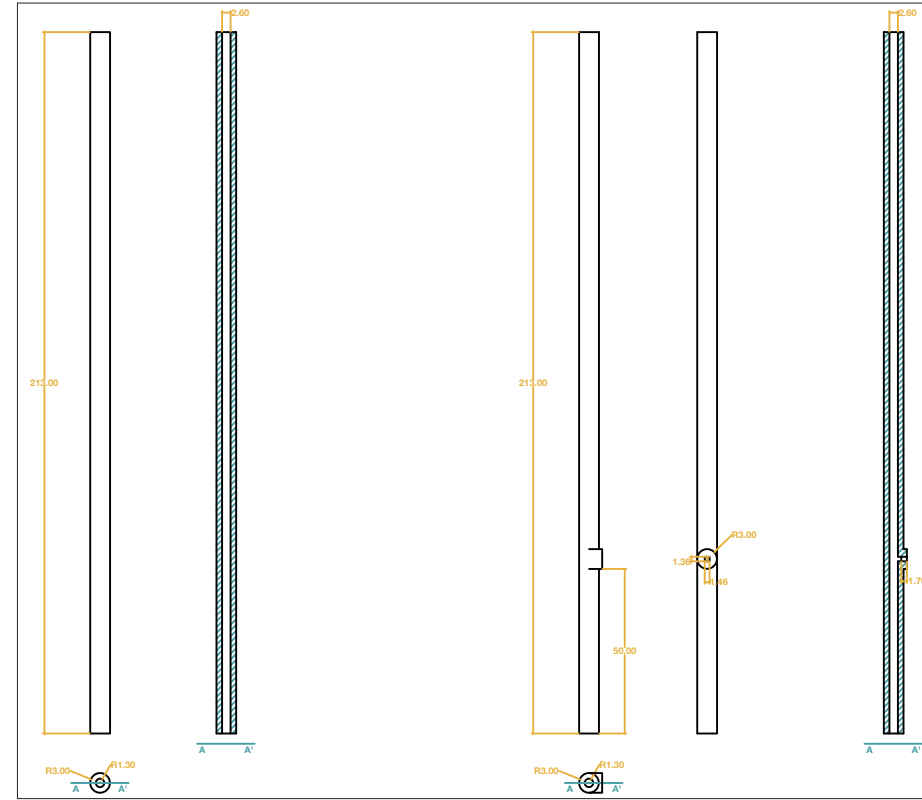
Planta, alzado y sección de la Columna 213 A y de la Columna 213 B.
